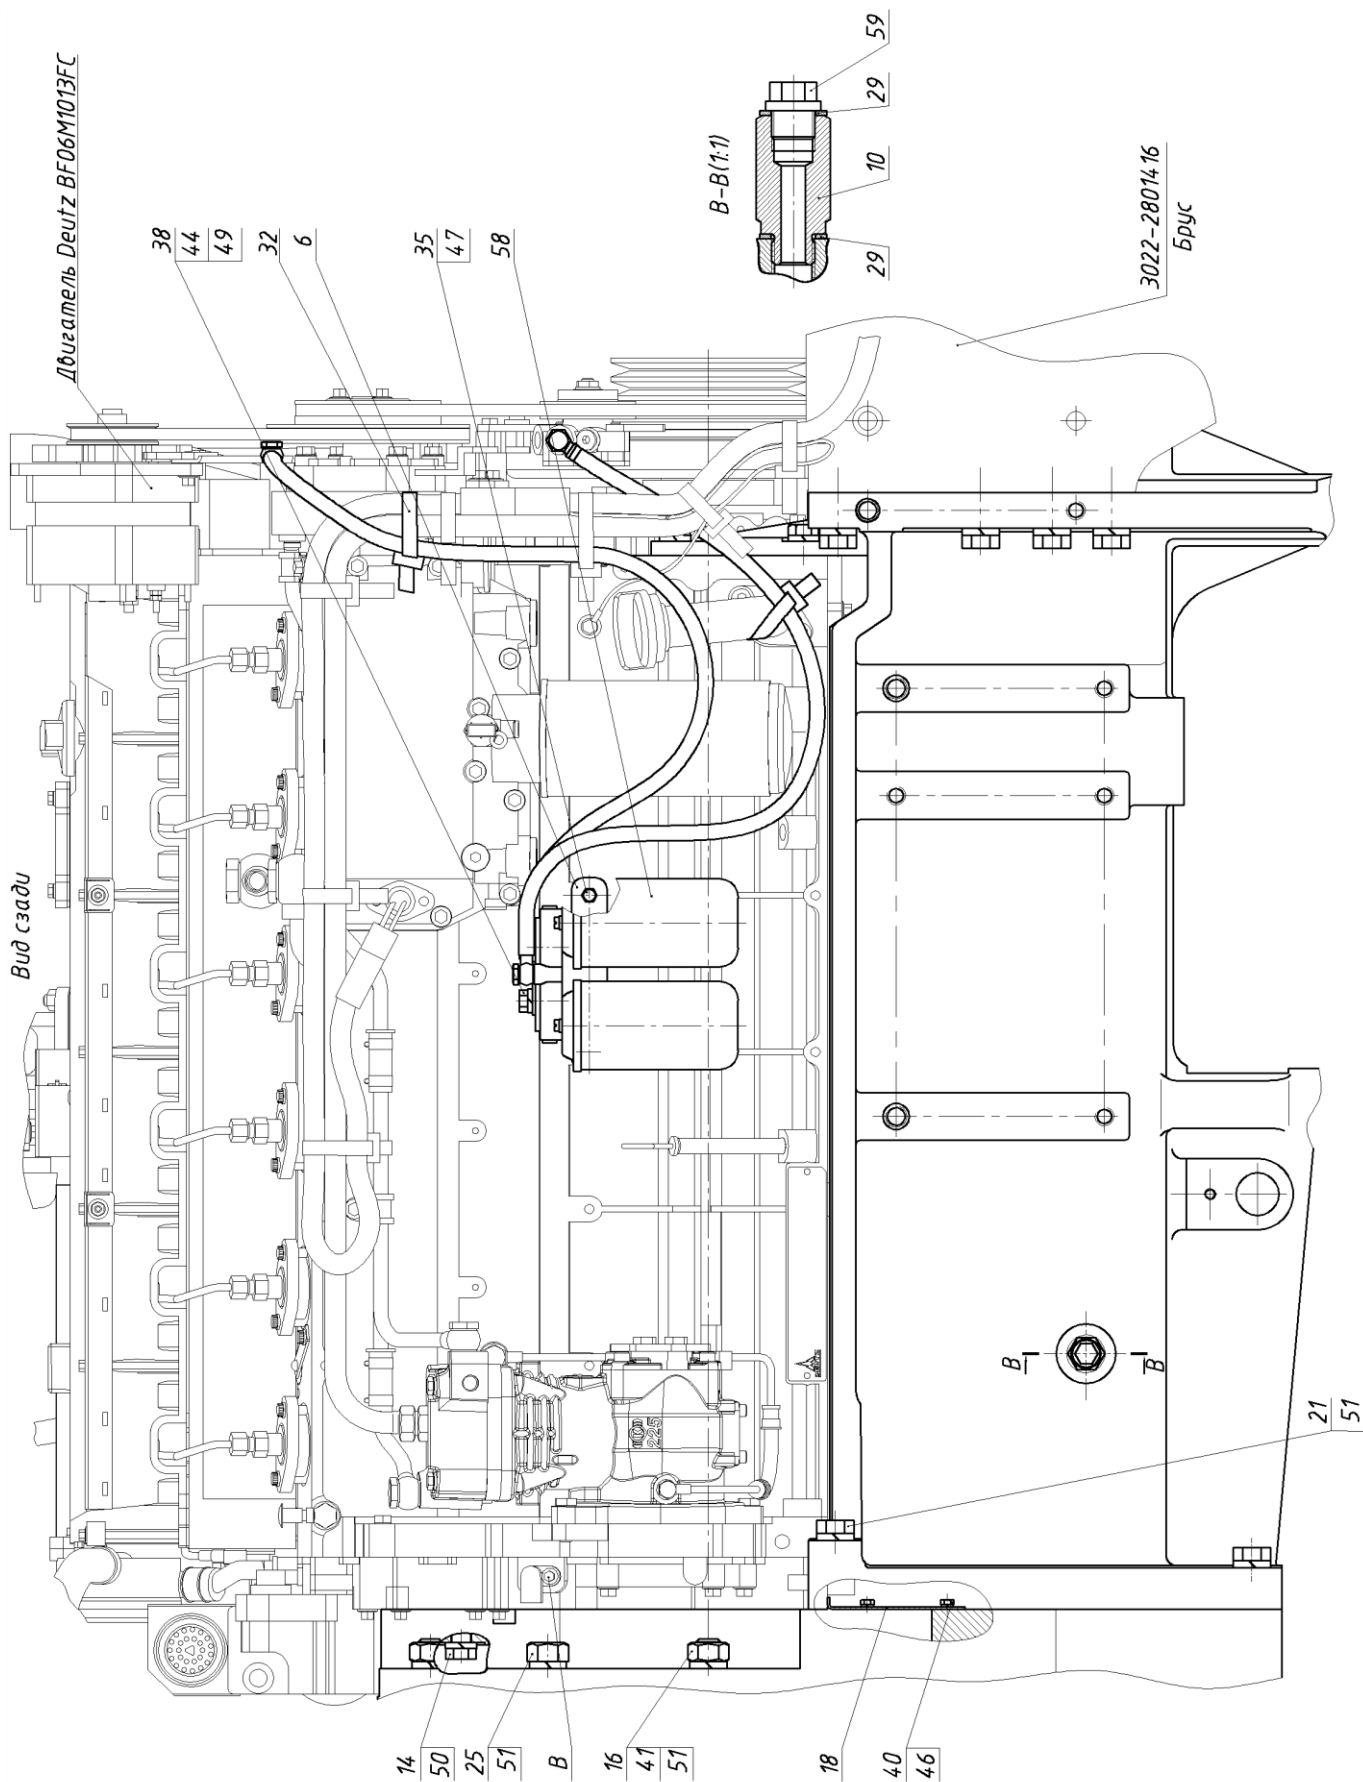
Установка двигателя (Беларус-3022.2)
